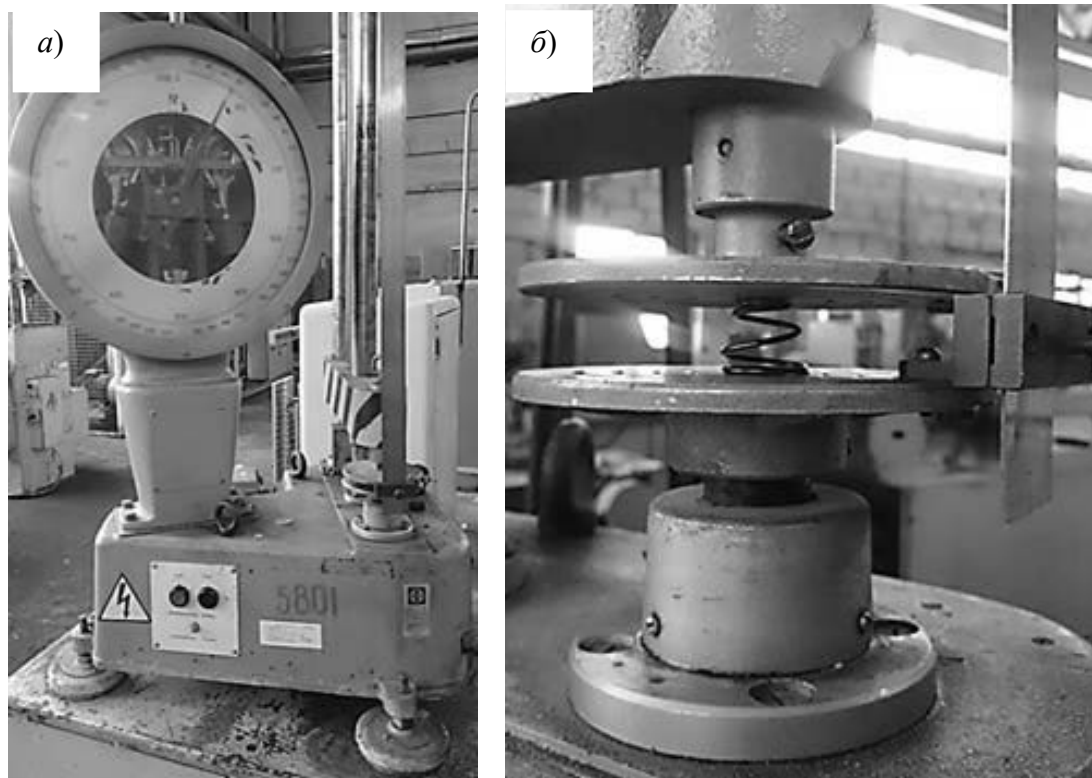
Машина для испытания пружин МИП-100-2: а – общий вид машины; б – испытание пружины поршневого узла амортизатора
